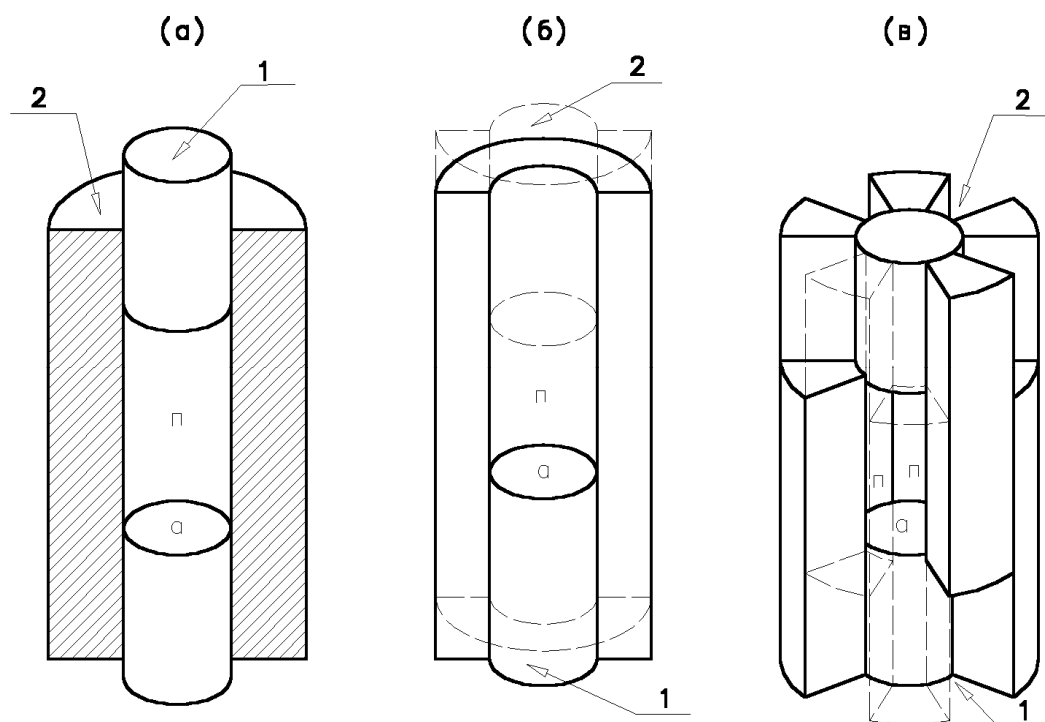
Способы прессования порошковых материалов в закрытых пресс-формах: (а) – одноосное одностороннее прессование; (б), (в) – коллекторный способ
